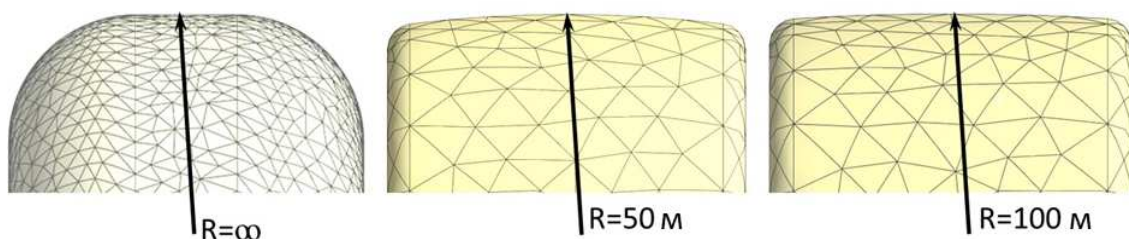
Робочі поверхні роликків механізму заряджання за варіювання радіусів «бочки» на твірній робочій боковій поверхні
